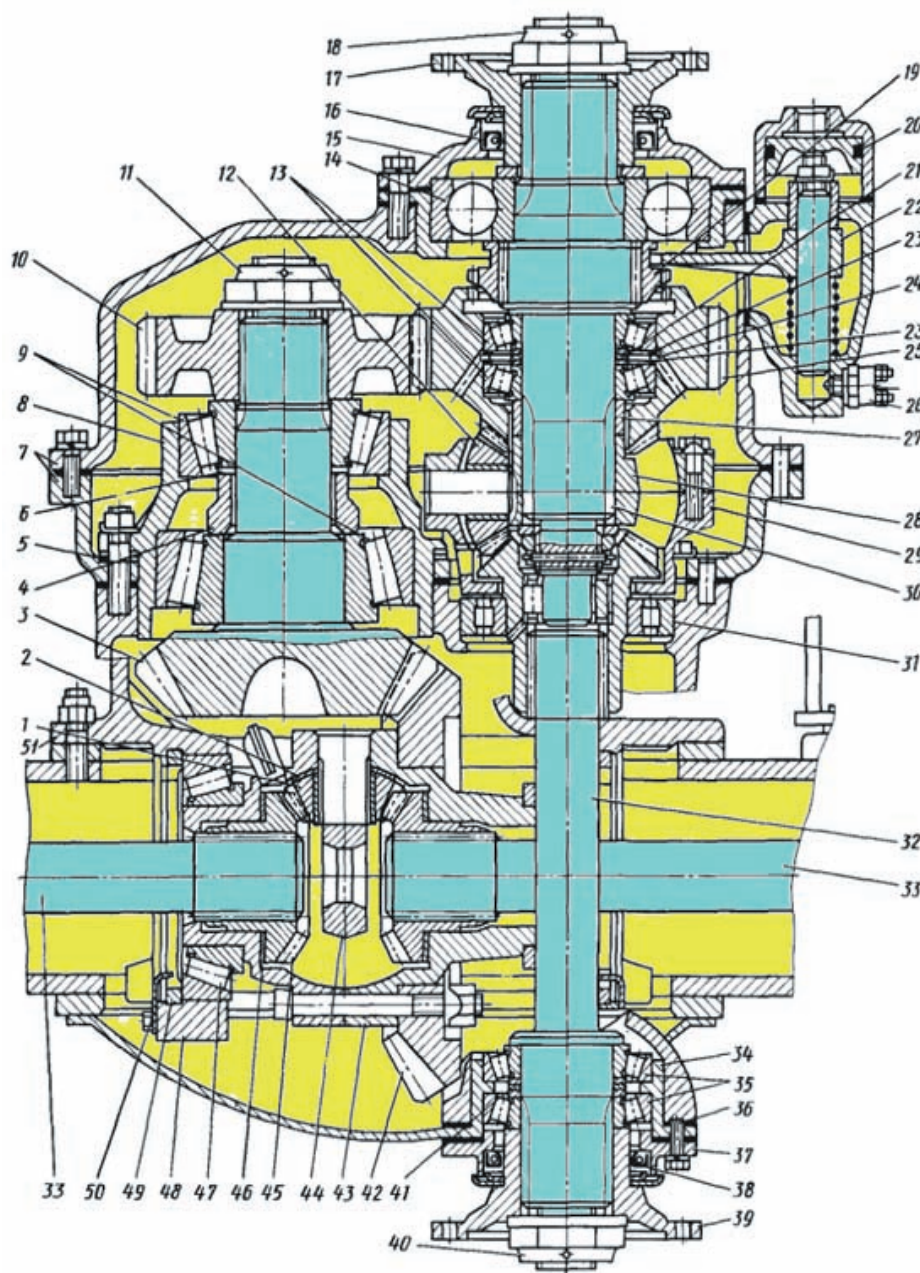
Центральный редуктор среднего моста: 1, 12 — са теллиты; 2, 46 — опорные шайбы; 3 — ведущая коническая шестерня; 4, 27 — распорные втулки; 5 — регулировочные прокладки; 6, 21, 41 — регулировочные шайбы; 7 — картеры; 8 — картер по подшипников; 9, 13, 14, 31, 35, 47 — подшипники; 10 — ведомая цилиндрическая шестерня; 11, 18, 40 — гайки; 15, 37 — крышки; 16, 38 — сальники; 17, 39 — фланцы; 19 — муфта блокировки межосевого дифференциала; 20 — механизм блокировки межосевого дифференциала; 22 — вилка включения муфты; 23 — упорная шайба; 24 — стопорная шайба; 25 — ведущая цилиндрическая шестерня; 26 — датчик включения блокировки межосевого дифференциала; 28, 44 — крестовины; 29 — межосевой дифференциал; 30 — вал привода мостов; 32 — выходной вал; 33 — полуось; 34 — стакан; 36 — болт; 42 — ведомая шестерня; 43 — межколесный дифференциал; 45 — полуосевая шестерня; 48 — крышка; 49 — гайка подшипника дифференциала; 50 — стопор; 51 — картер редуктора
